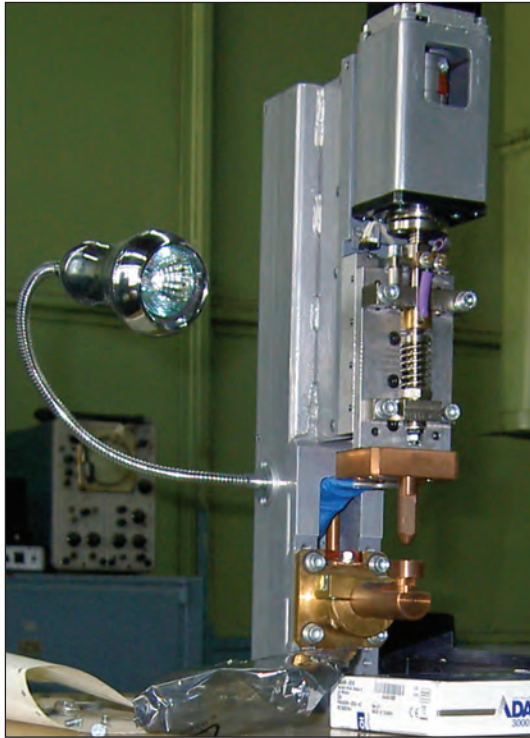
Сварочная головка машины МТЧ-5.05
